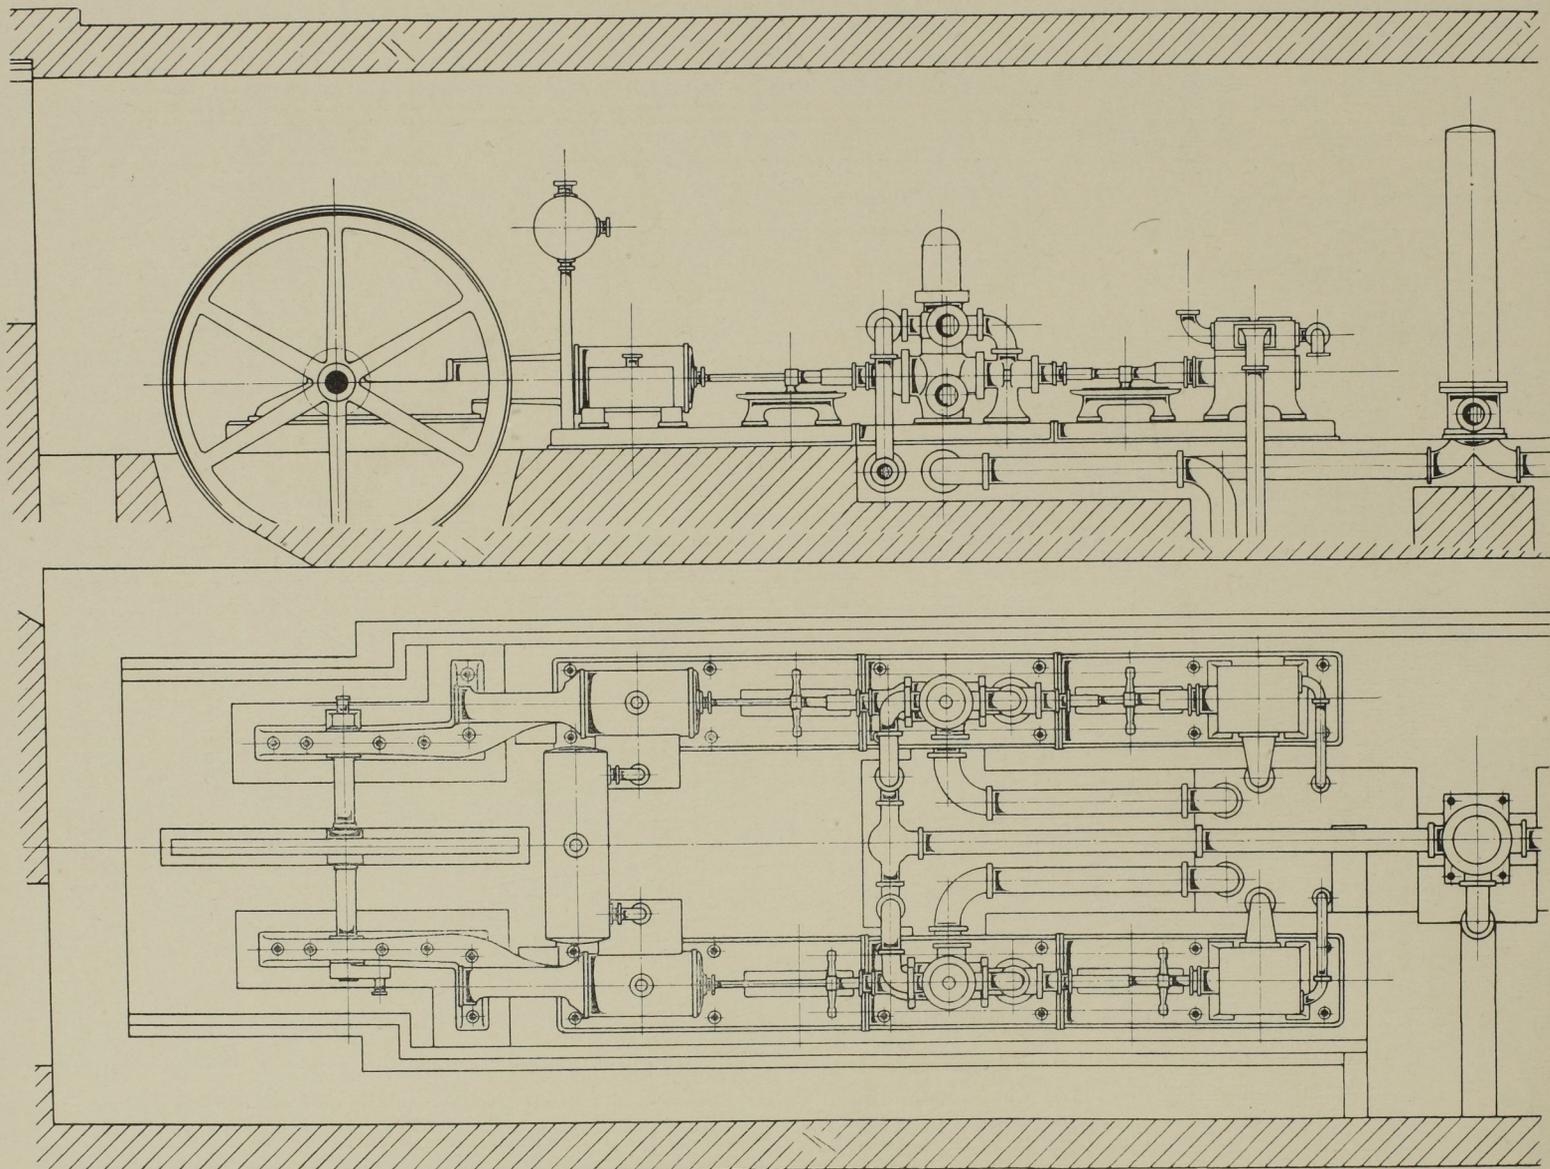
Seitenansicht und Grundriss der Maschine. Masst. 1:75.
